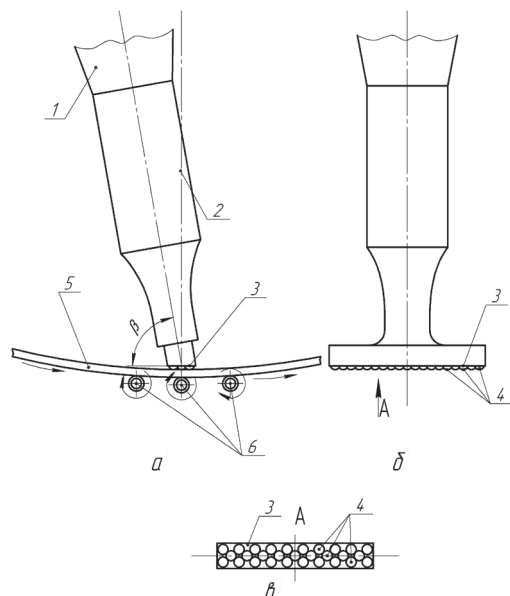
Устройство для поверхностного ультразвукового упрочнения закрепленными деформирующими элементами
